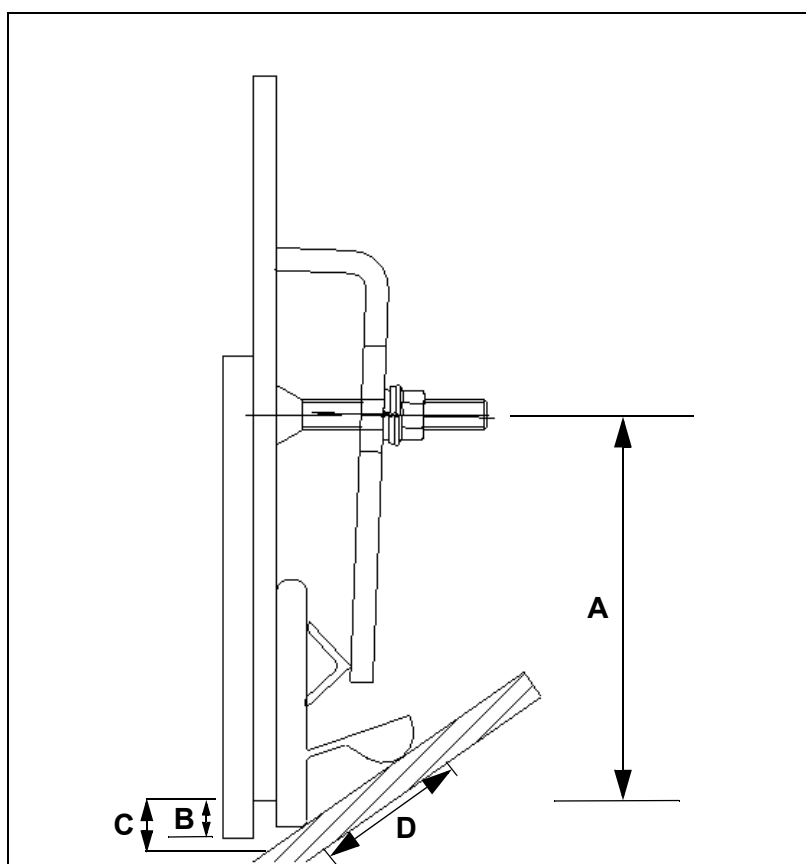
Dimensions d'installation du système d'étanchéité latéral
